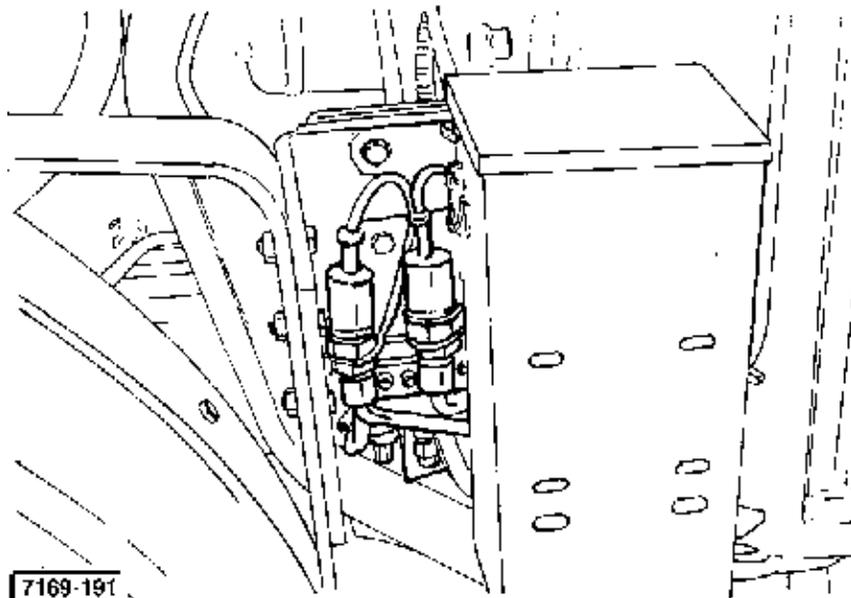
Prises hydrauliques situées côté droit du poste de conduite
